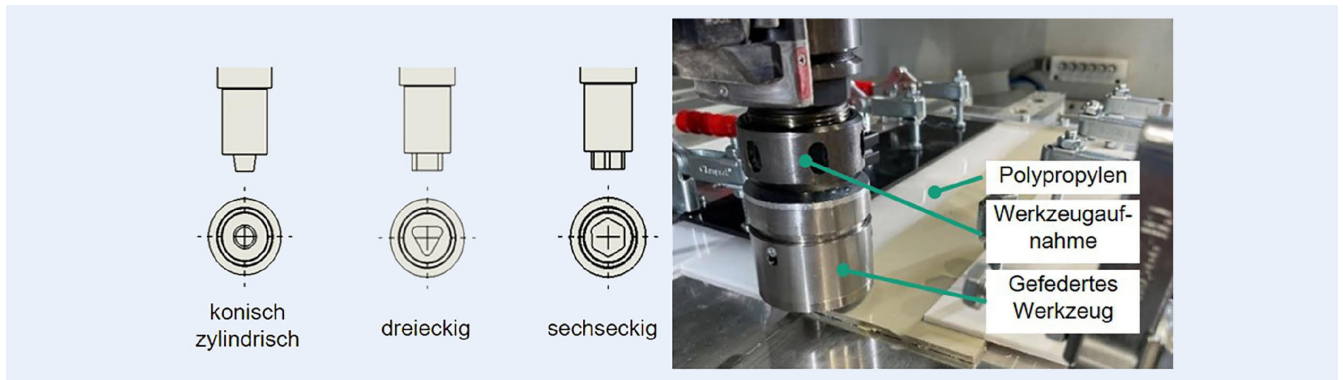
Verwendete Werkzeugpins (links) und Versuchsaufbau (rechts). Foto: Fraunhofer IPA
